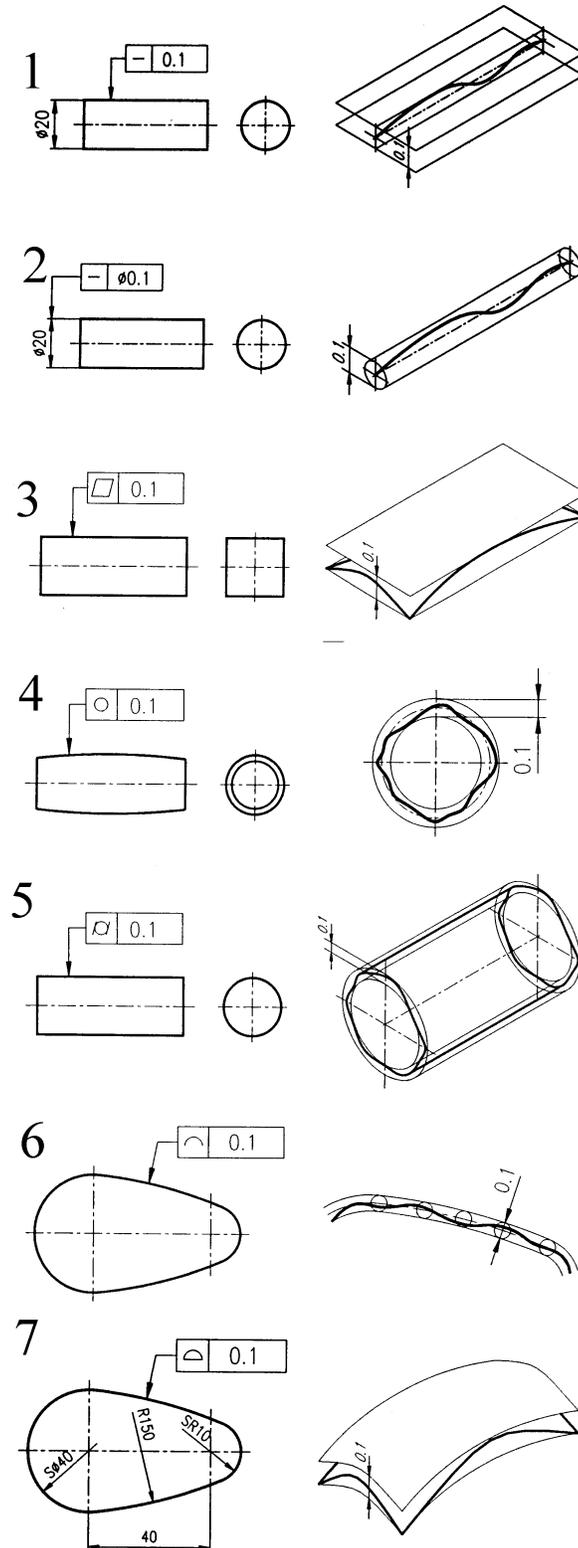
Ejemplos de tolerancias geométricas.
